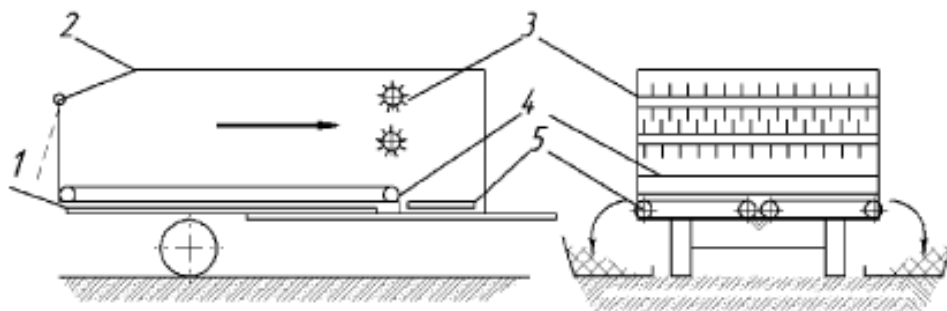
Кормороздавач РММ-Ф-6 [8]: 1 – рама; 2 – кузов; 3 – бітер; 4 – поздовжній транспортер; 5 – поперечний транспортер
